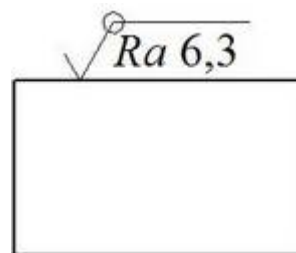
Схема обозначения одинаковой шероховатости поверхностей, образующих контур
